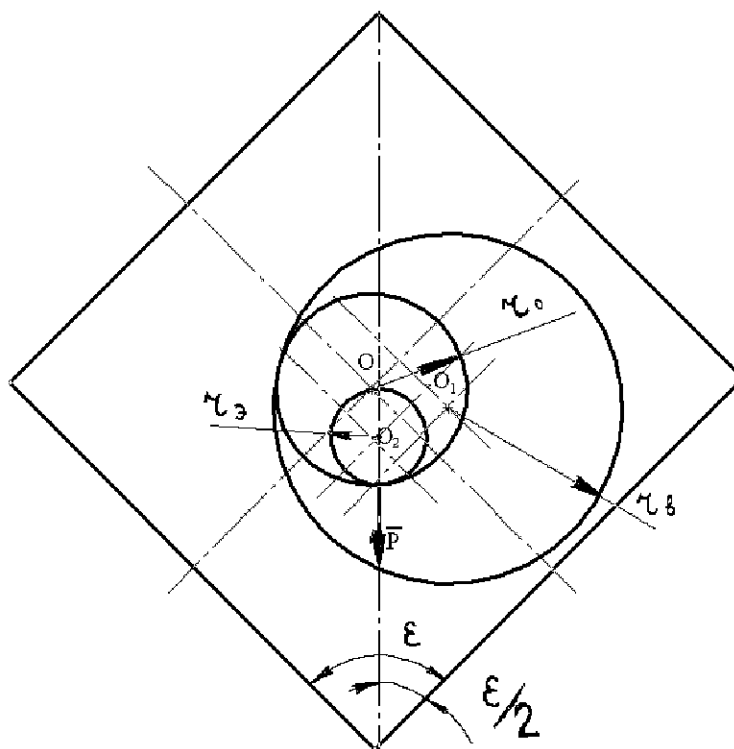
Расчетная схема эксцентрического закрепления
